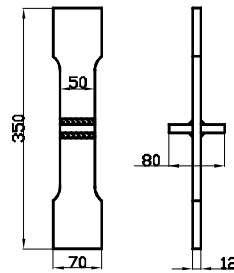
Форма та розміри зразка таврового зварного з'єднання сталі 09Г2С
